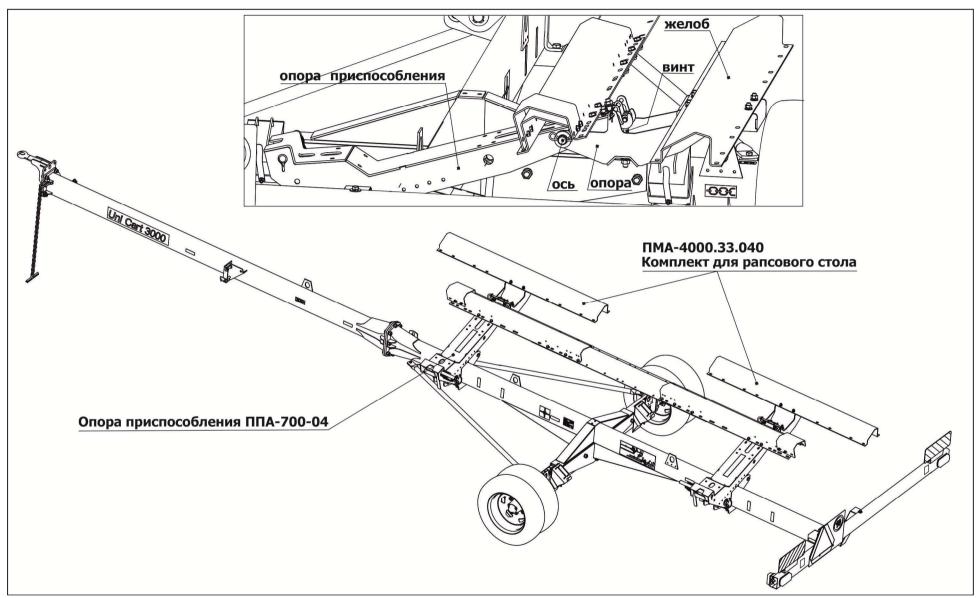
Установка комплекта для рапсового стола ПМА-4000.33.040 на приспособление ППА-700-04
